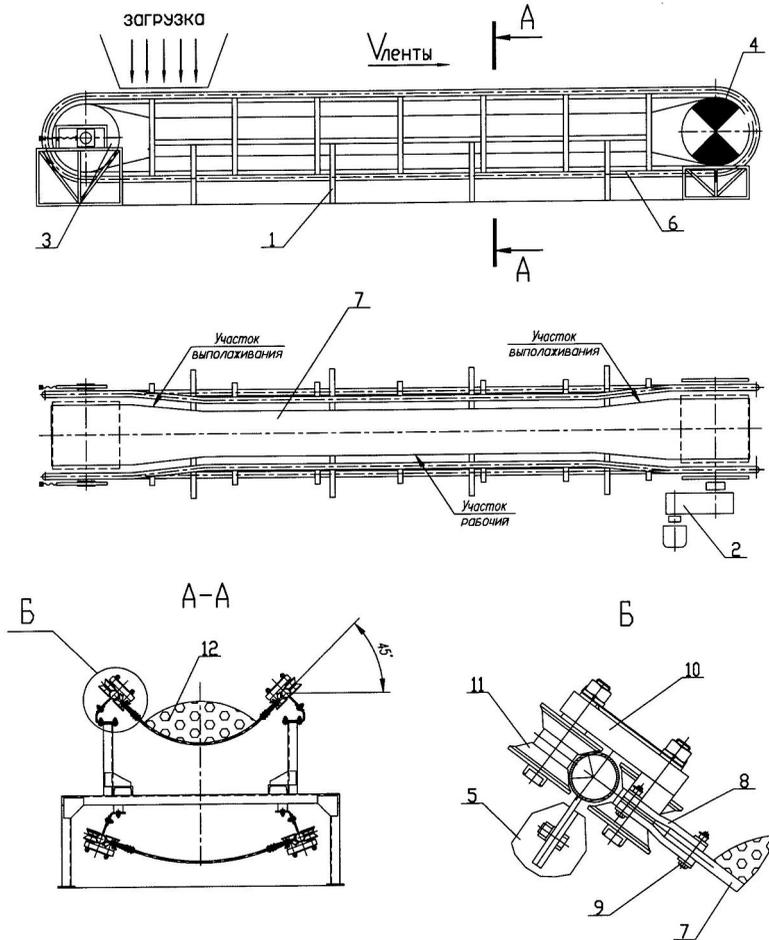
Конвейер с подвесной лентой: 1 – став; 2 – привод; 3 – натяжной барабан; 4 – приводной барабан; 5 – лента; 6 – трубчатые направляющие; 7 – узел крепления; 8 – кронштейн; 9 – ролик; 10 – подвеска; 11 – гибкие «ленточки»; 12 – груз
